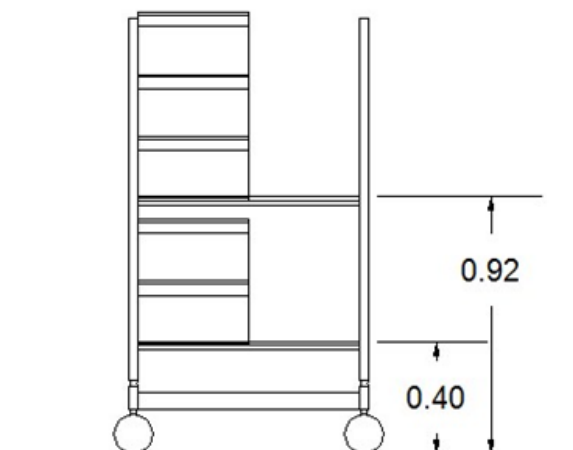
Proposta de reestruturação da carruagem (medidas em metros).
